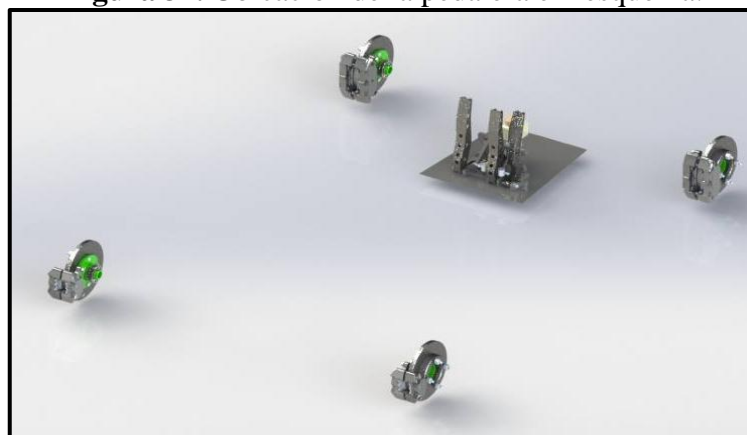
Acoplamiento del conjunto disco pastilla del monoplaza al chasis
